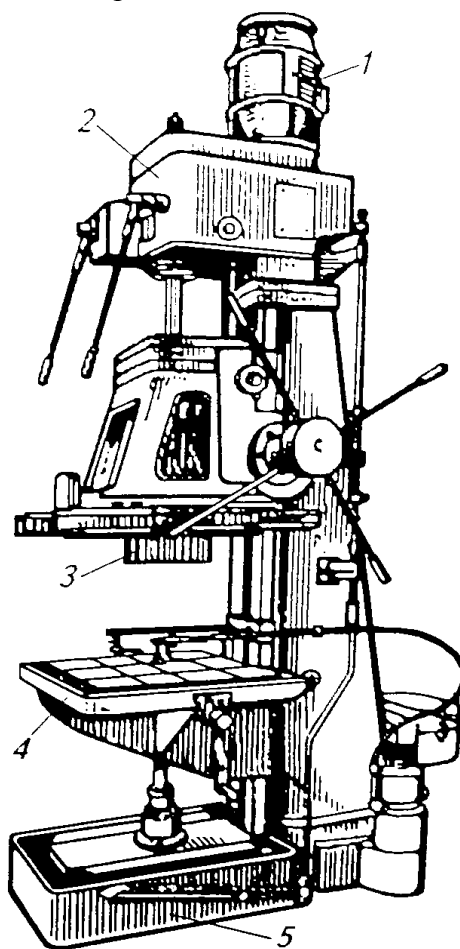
Общий вид вертикально – сверлильного станка: 1 – электродвигатель привода; 2 – редуктор; 3 – шпиндель; 4 – вертикально перемещаемый стол; 5 – станина.
